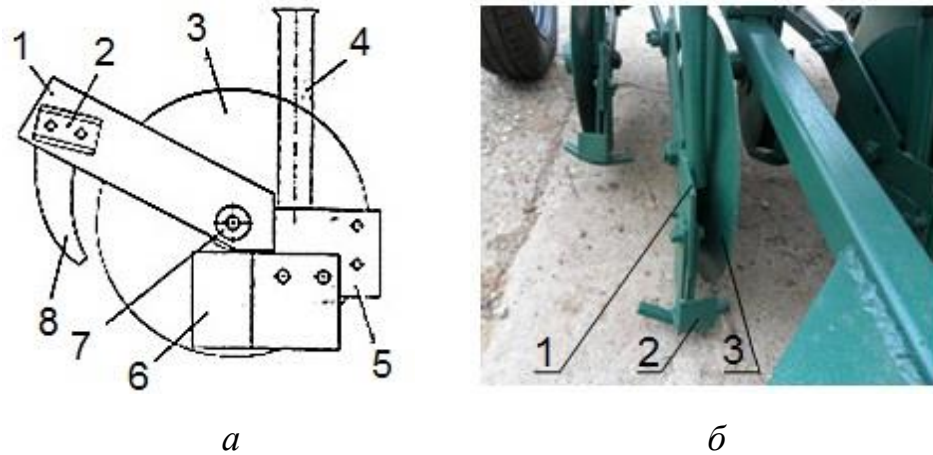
Конструктивна схема а і загальний вигляд однодисково-анкерного сошника сівалки СФС-2:
